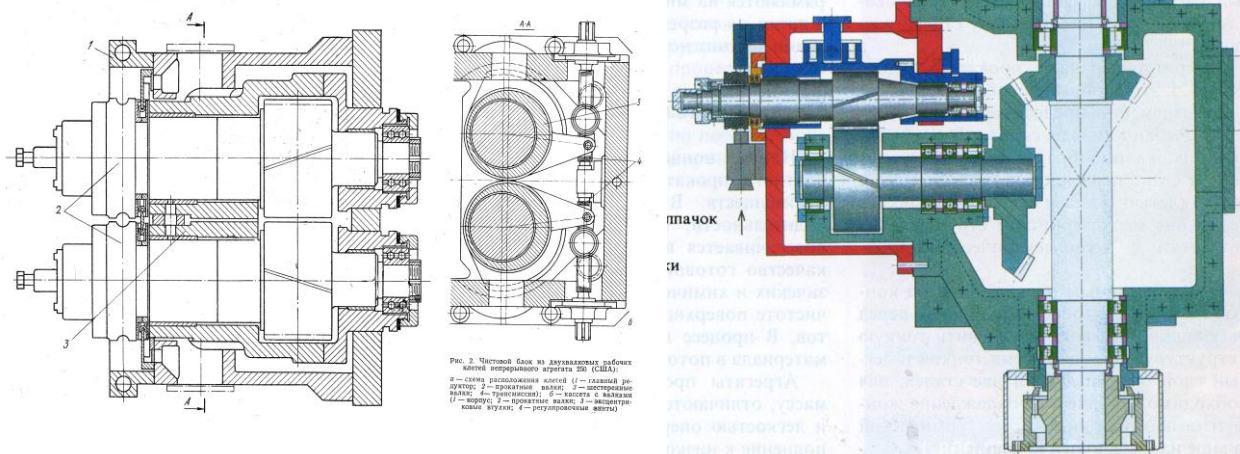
Схематична конструкція модуля проволочного блоку
